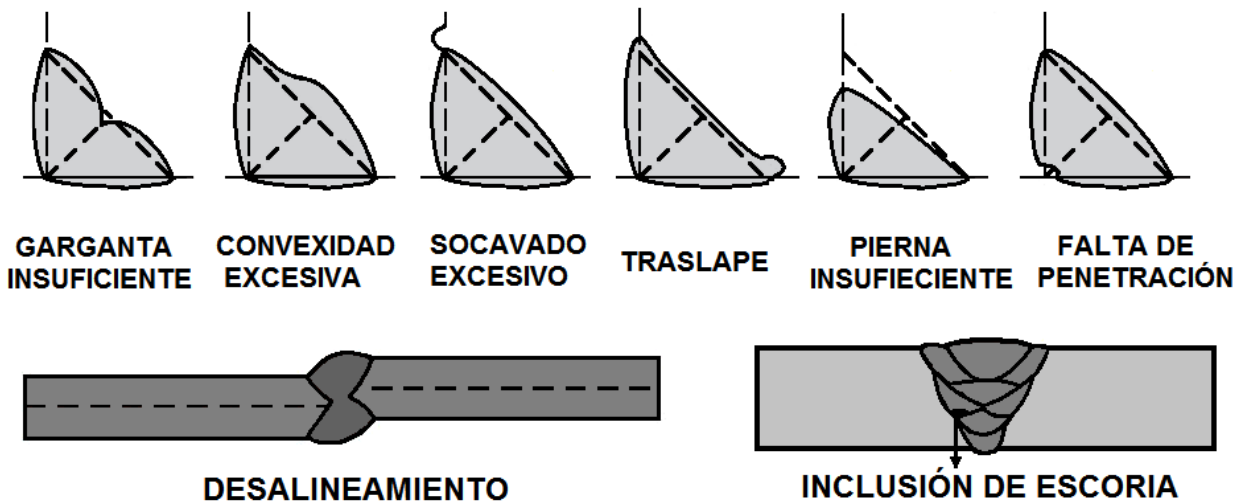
Defectos que pueden presentar las soldaduras (8, 18, 86)
